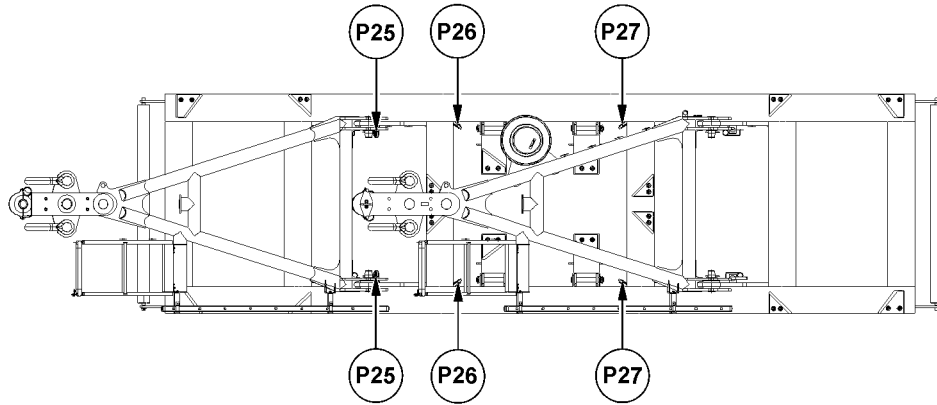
Pontos de fixação da paleta do lastro em suspensão, vista de cima, cavaletes de montagem pousados
